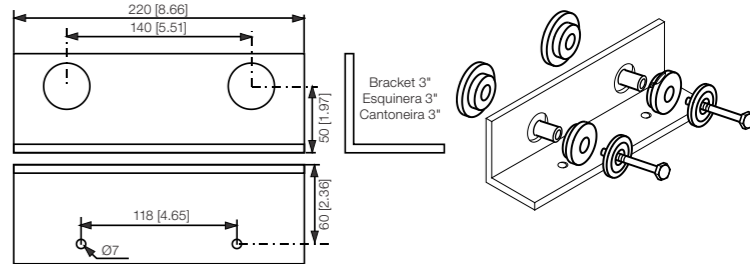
Bracket in L - Dimensiones in millimeters [inches]
